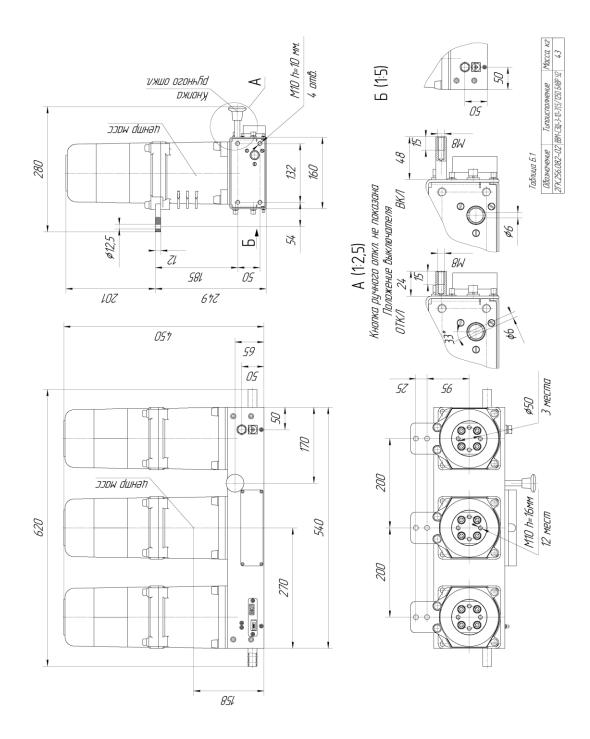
Габаритные, присоединительные и установочные размеры выключателя типа BBM-СЭЩ-3-10-31,5/1250 БАВР У2
